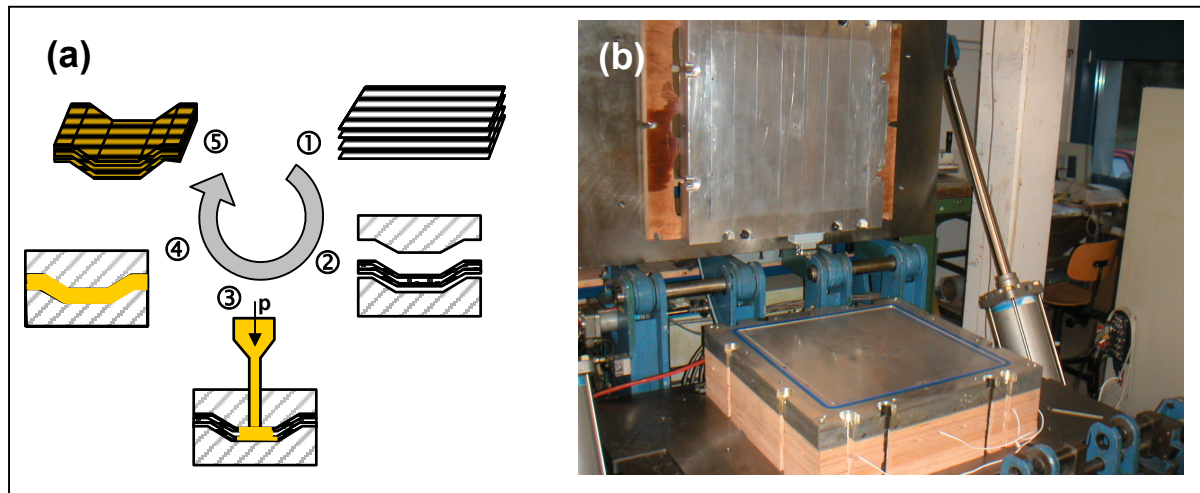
(a) RTM-Verfahren (schematisch); (b) Werkzeugträger mit Plattenwerkzeug
